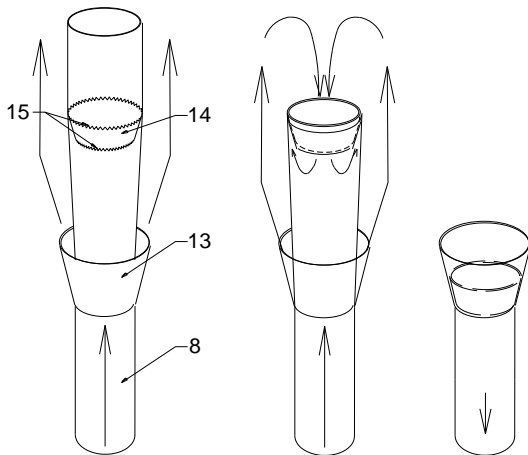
Способ крепления рукава со съёмным фиксатором
